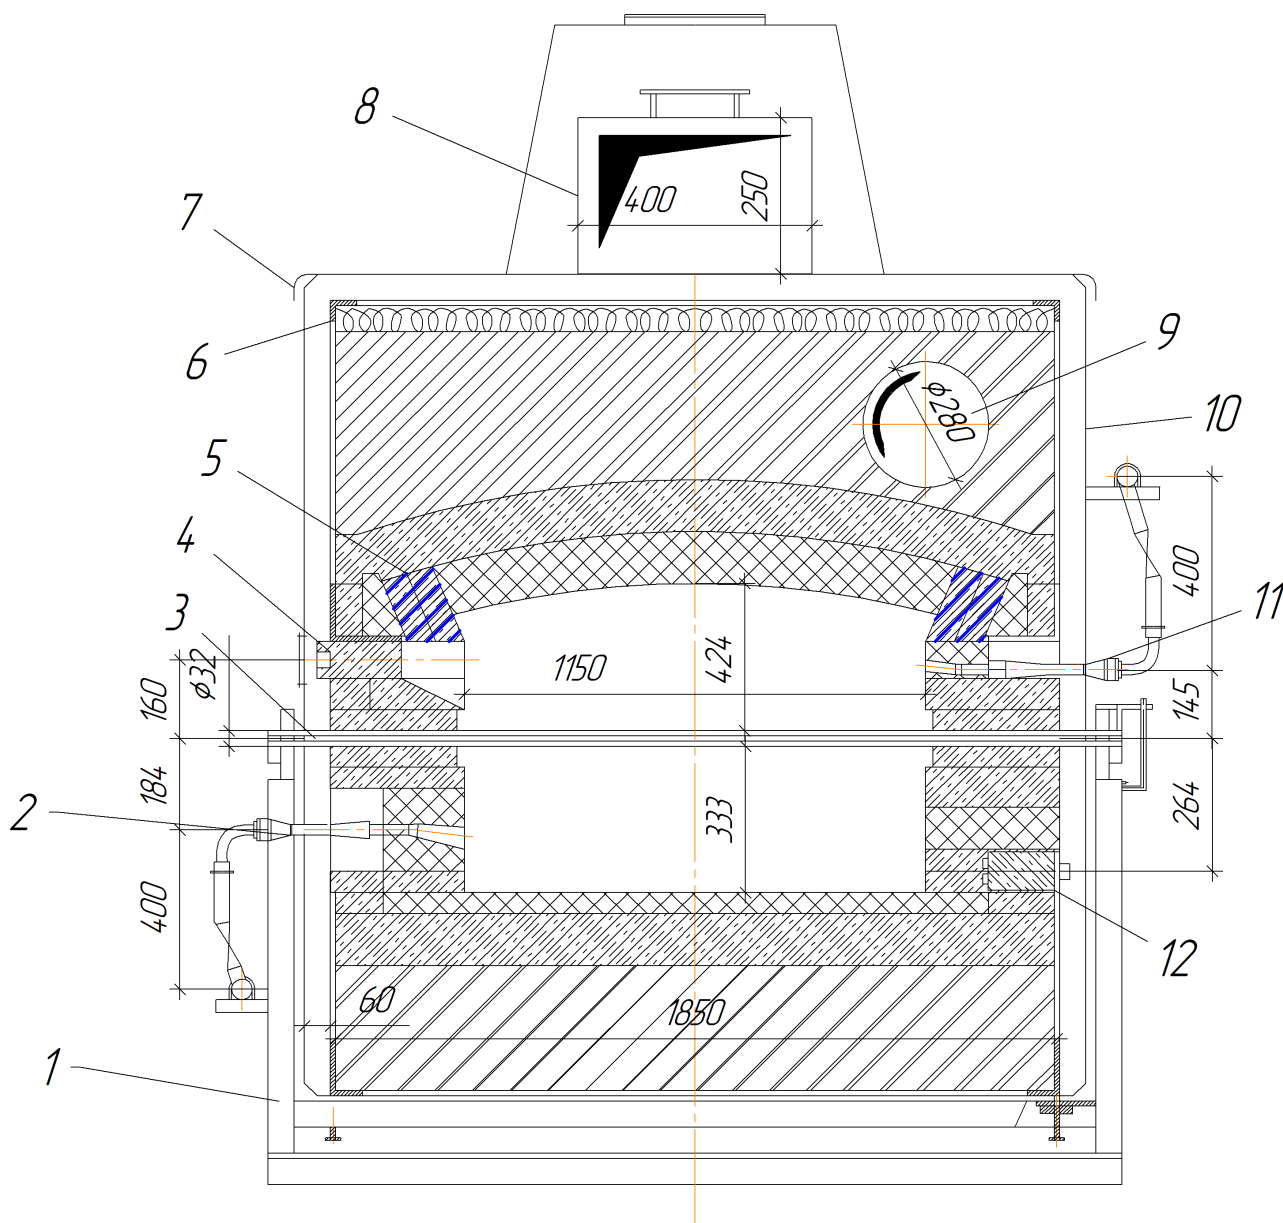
Поперечное сечение щелевой печи: 1— рама роликового конвейера; 2 — нижняя горелка; 3 — транспортирующий ролик; 4 — смотровое отверстие; 5 — футеровка; 6 — корпус; 7 — верхнее укрытие; 8 — вентиляционный коллектор; 9 — газоход; 10 — экран; 11 — верхняя горелка; 12 — люк для очистки пода
